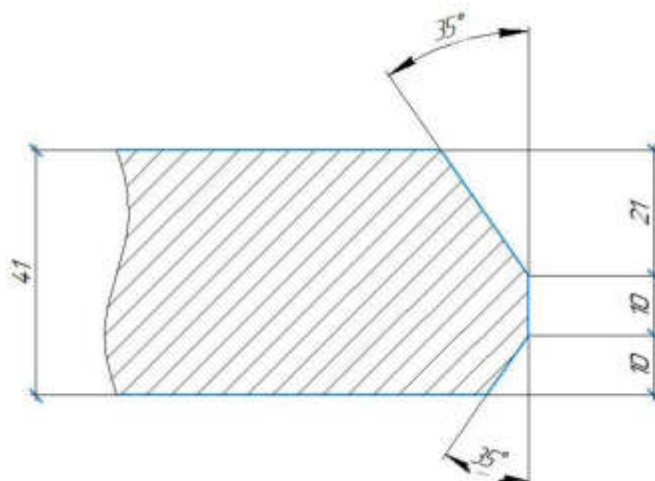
Фаски для сварки двумя дугами
